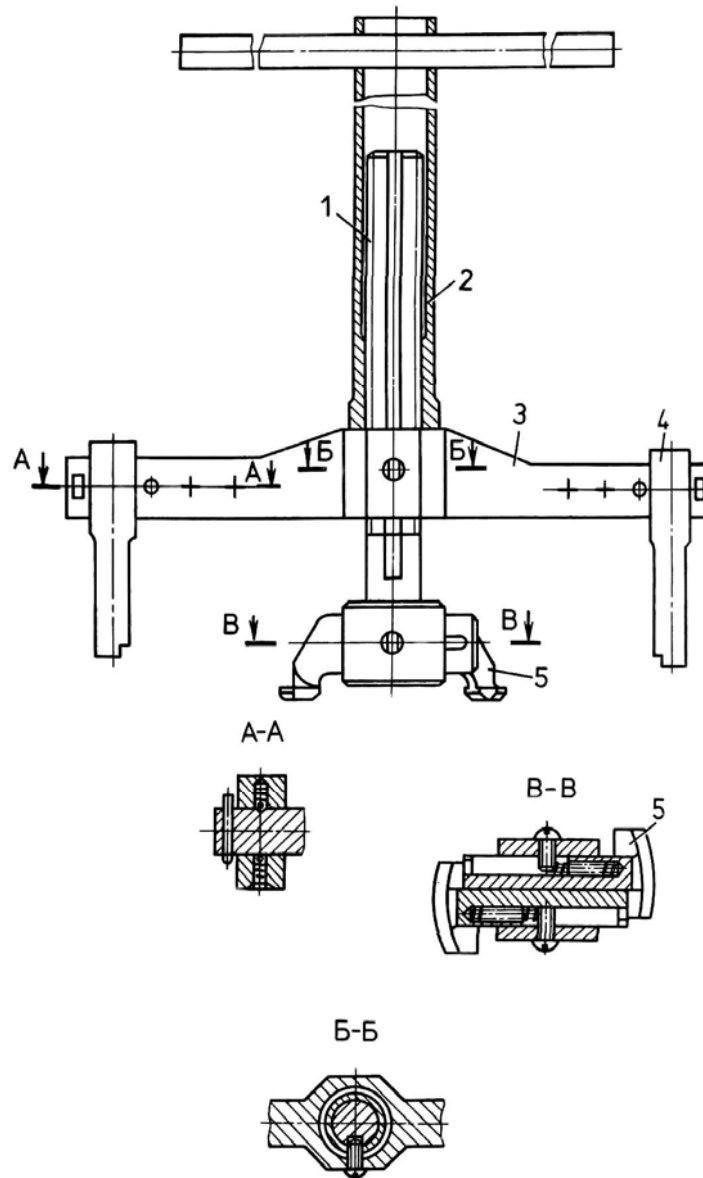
Съемник для выпрессовки наружных колец из ступиц колес:
